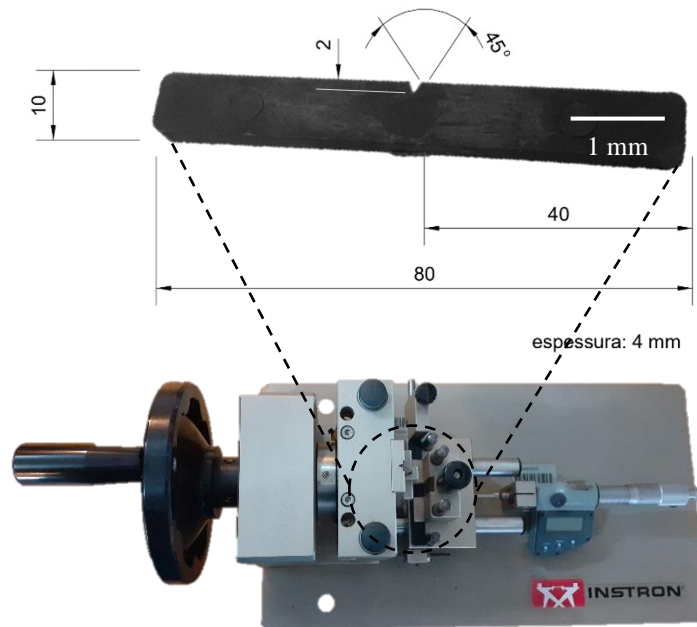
Geometria e dimensões do corpo de prova padrão de impacto ensaiado
